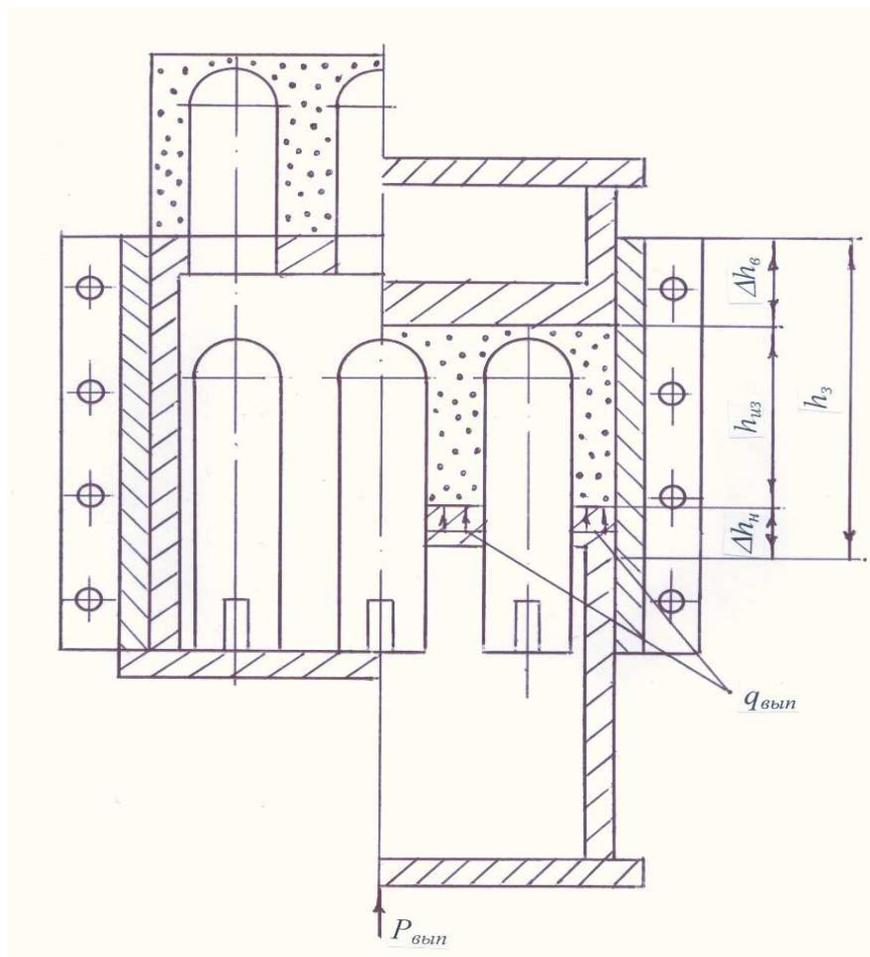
Расчетная схема процесса выпрессовки отформованного изделия из матрицы.
